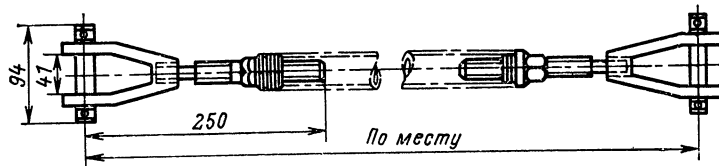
Штанга редуктора малой модели ШРМ.
